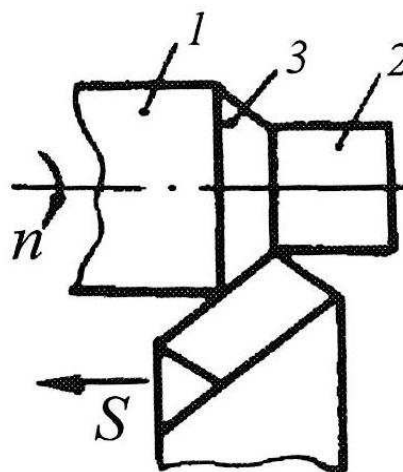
Поверхні на заготовці, яка обробляється точінням
